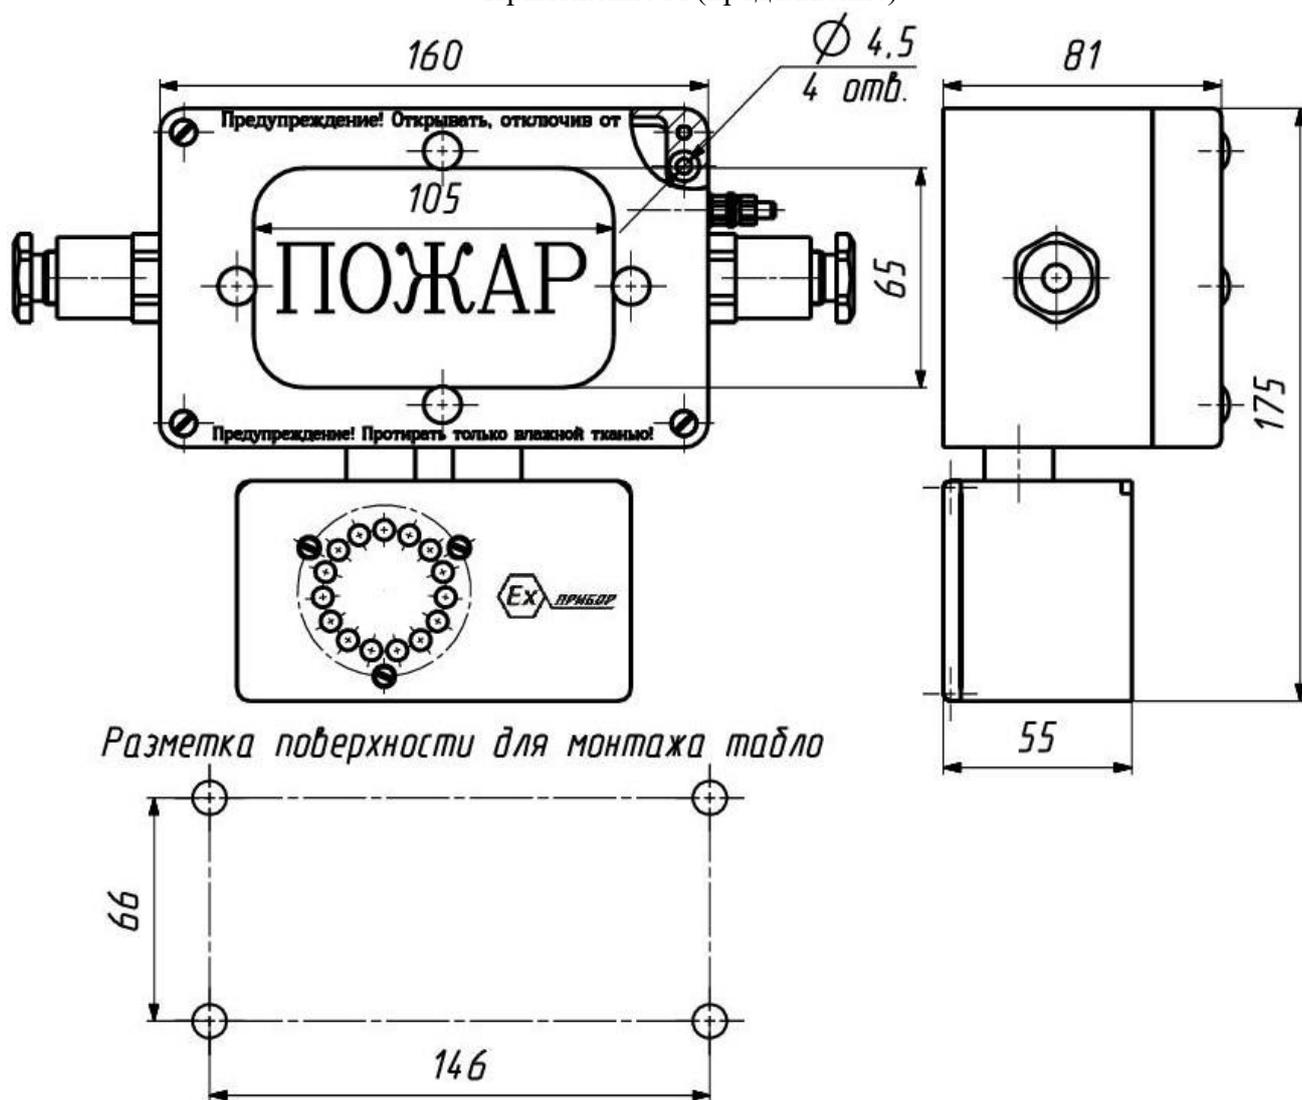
Общий вид с элементами обеспечения взрывозащиты, габаритные, присоединительные размеры табло световой модели ExTK-3 (Остальное см. Рис. А.5, А.7)
